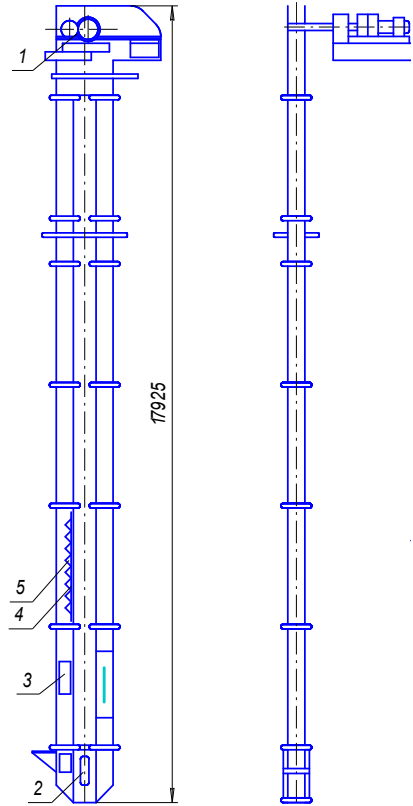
Элеватор ковшовый вертикальный ленточный типа Т-194
